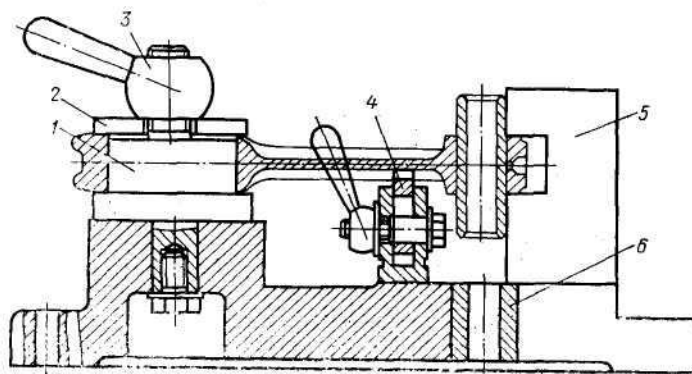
Приспособление для контроля и рихтовки шатунов:
